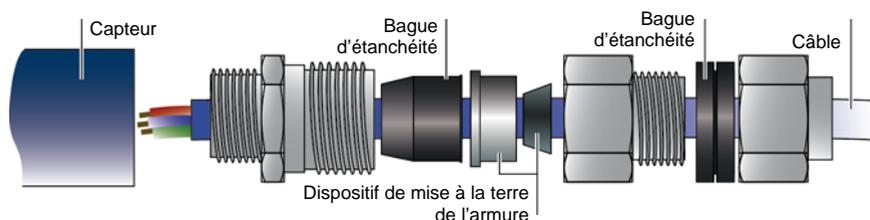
exemple de presse étoupe double compression pour serrage sur câble armé.
